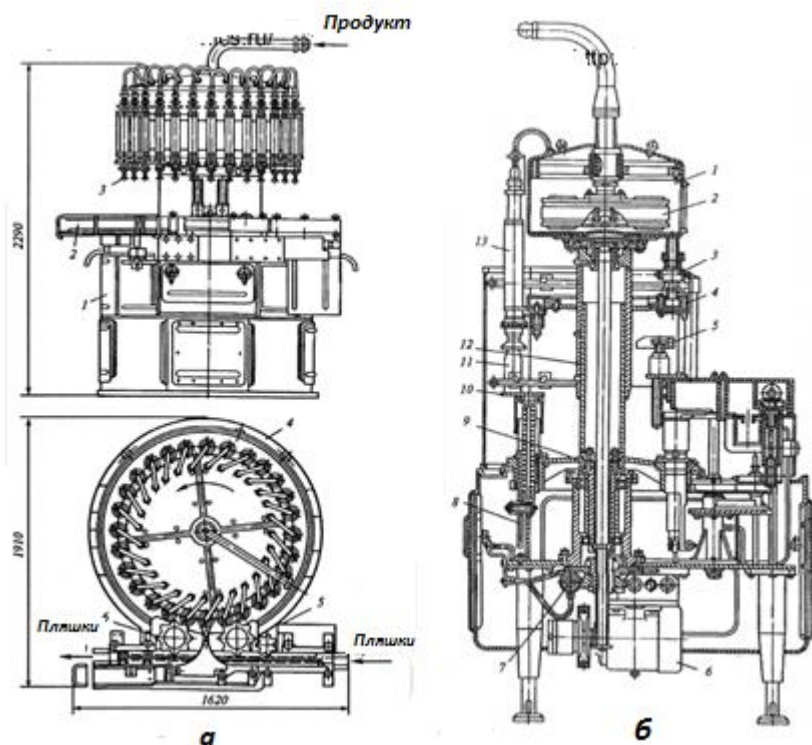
Дозувально-фасувальна машина ВРА-6А: а – загальний вигляд: 1 – станина; 2 – транспортер; 3 – дозувальний пристрій; 4 – ротор; 5, 6 – завантажувальна та розвантажувальна зірочки; б – розріз: 1 – резервуар; 2 – поплавець; 3 – кран; 4 – колектор; 5 – копір верхній; 6 – електродвигун; 7 – черв'ячний редуктор; 8 – копір нижній; 9 – ротор головного валу; 10 – підйомні столики; 11 – пляшки; 12 – телескопічна стійка; 13 – дозувальні пристрої
